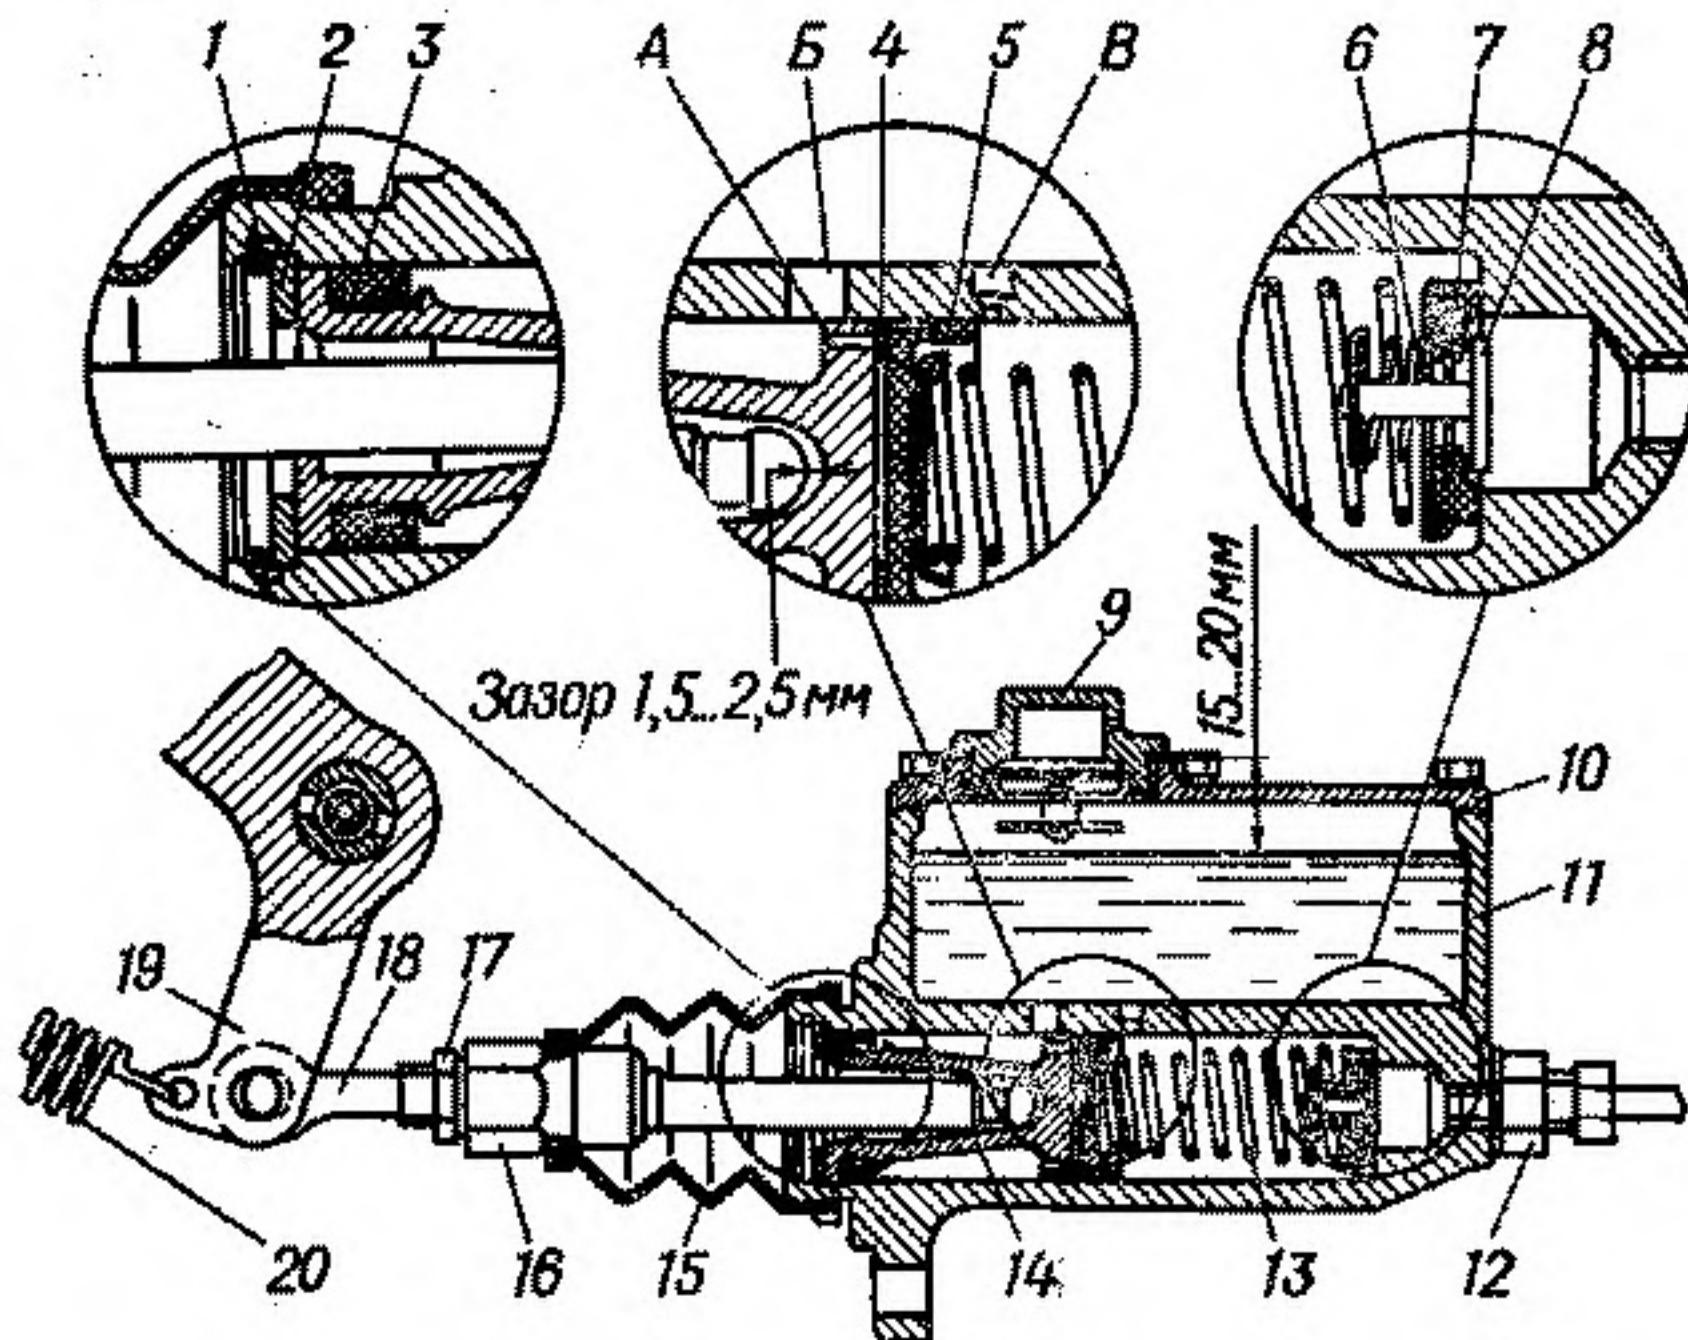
Главный цилиндр гидравлического привода тормоза:
